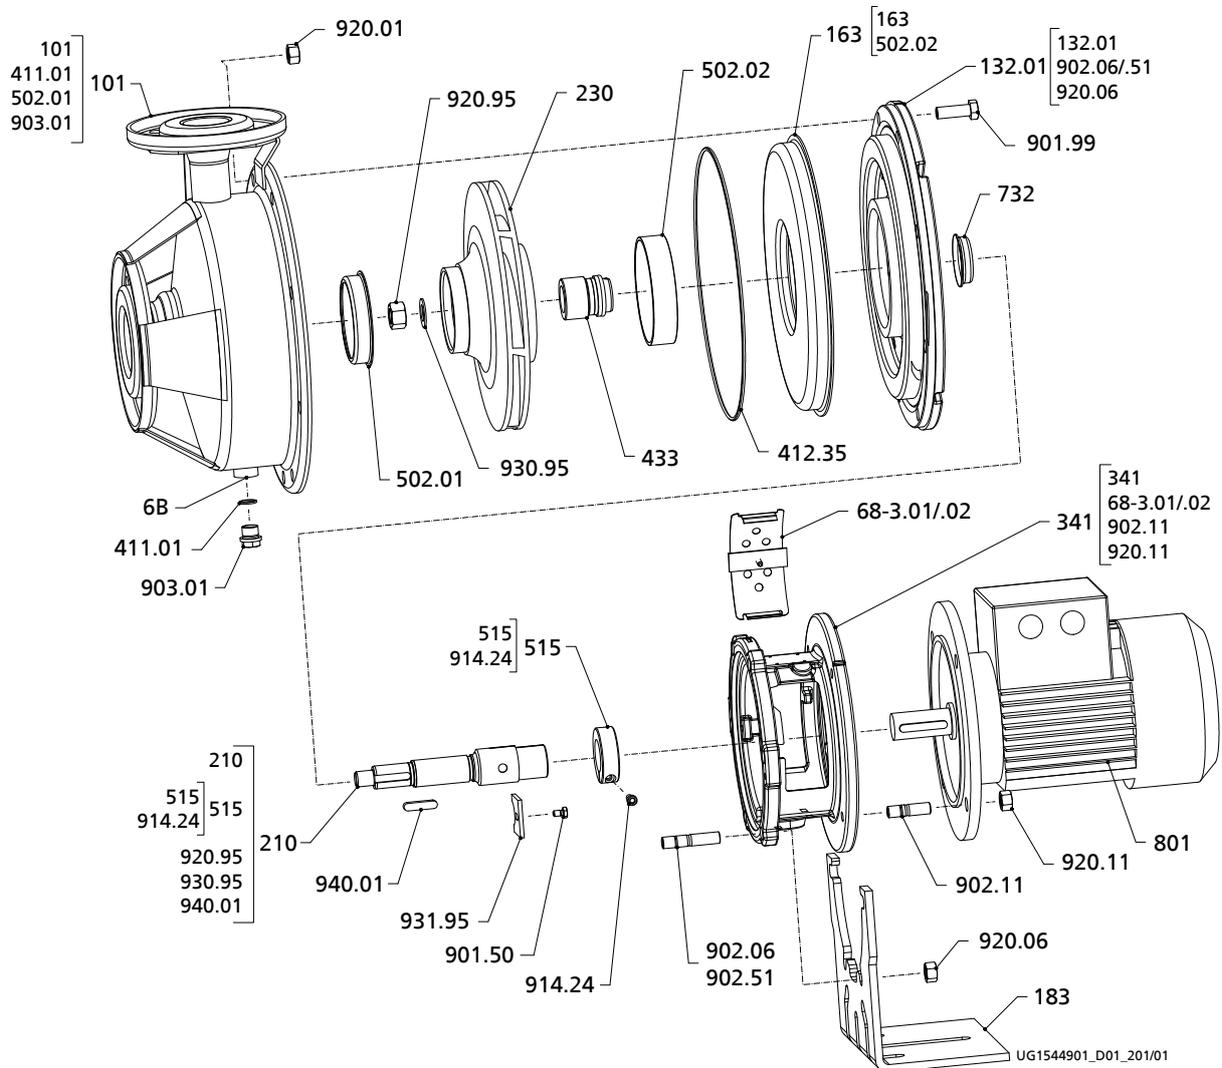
Explosionszeichnung Ausführung mit Welleneinheit 25.2
